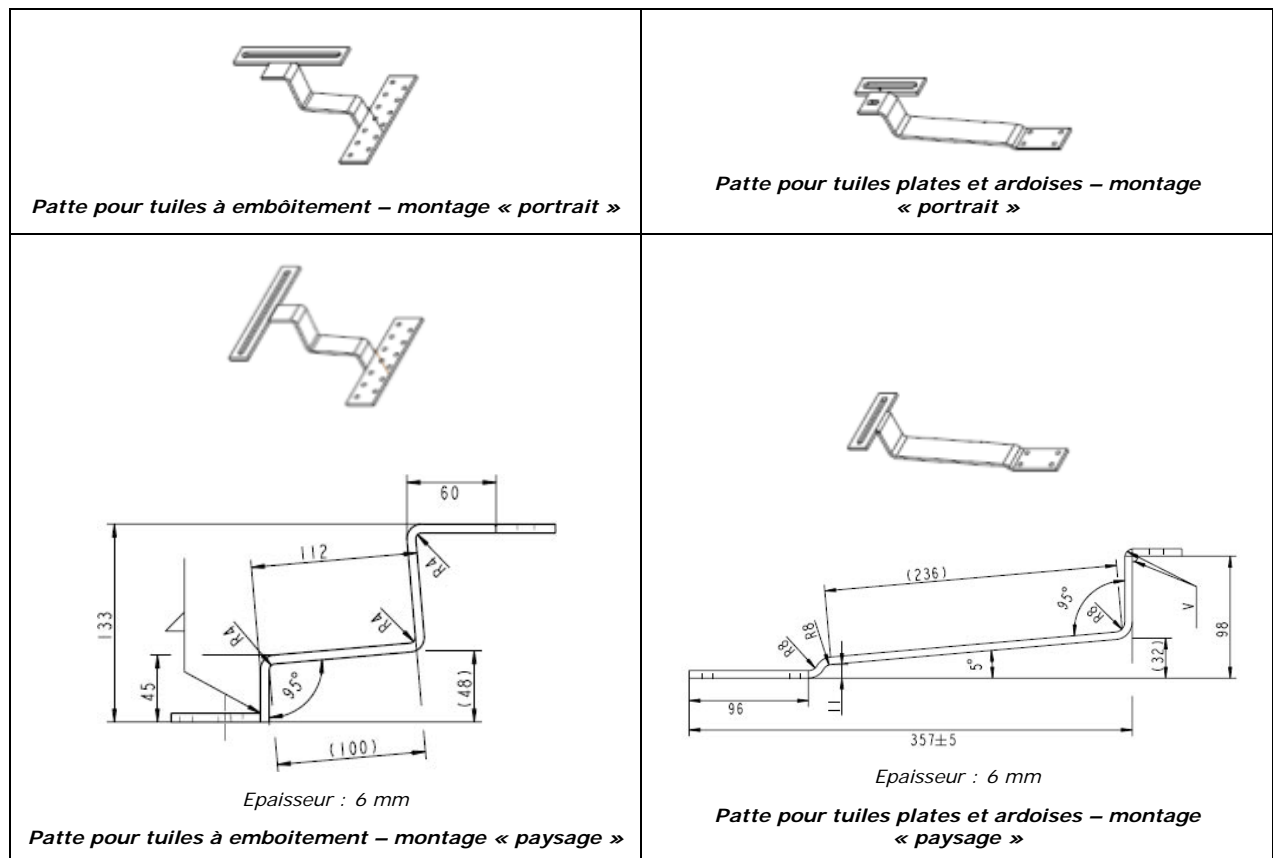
Pattes de fixation pour installation en surimposition toiture
